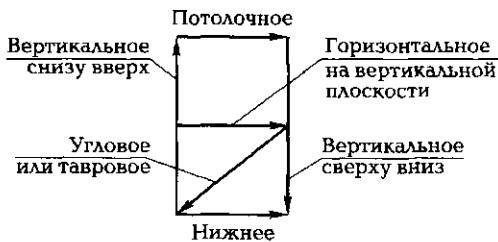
Схема указания пространственных положений сварки для покрытых электродов
